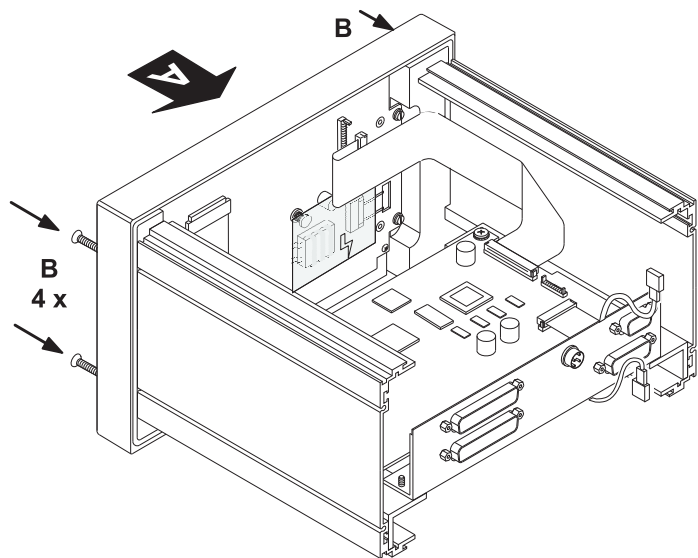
Ansetzen und Befestigen der Frontblende am Gehäuserahmen
